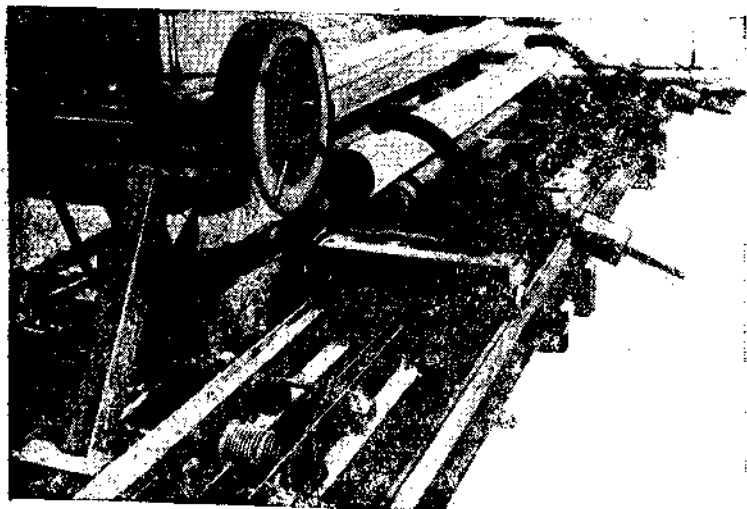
Конструкция окорочного станка ЦНИИМЭ В-2
